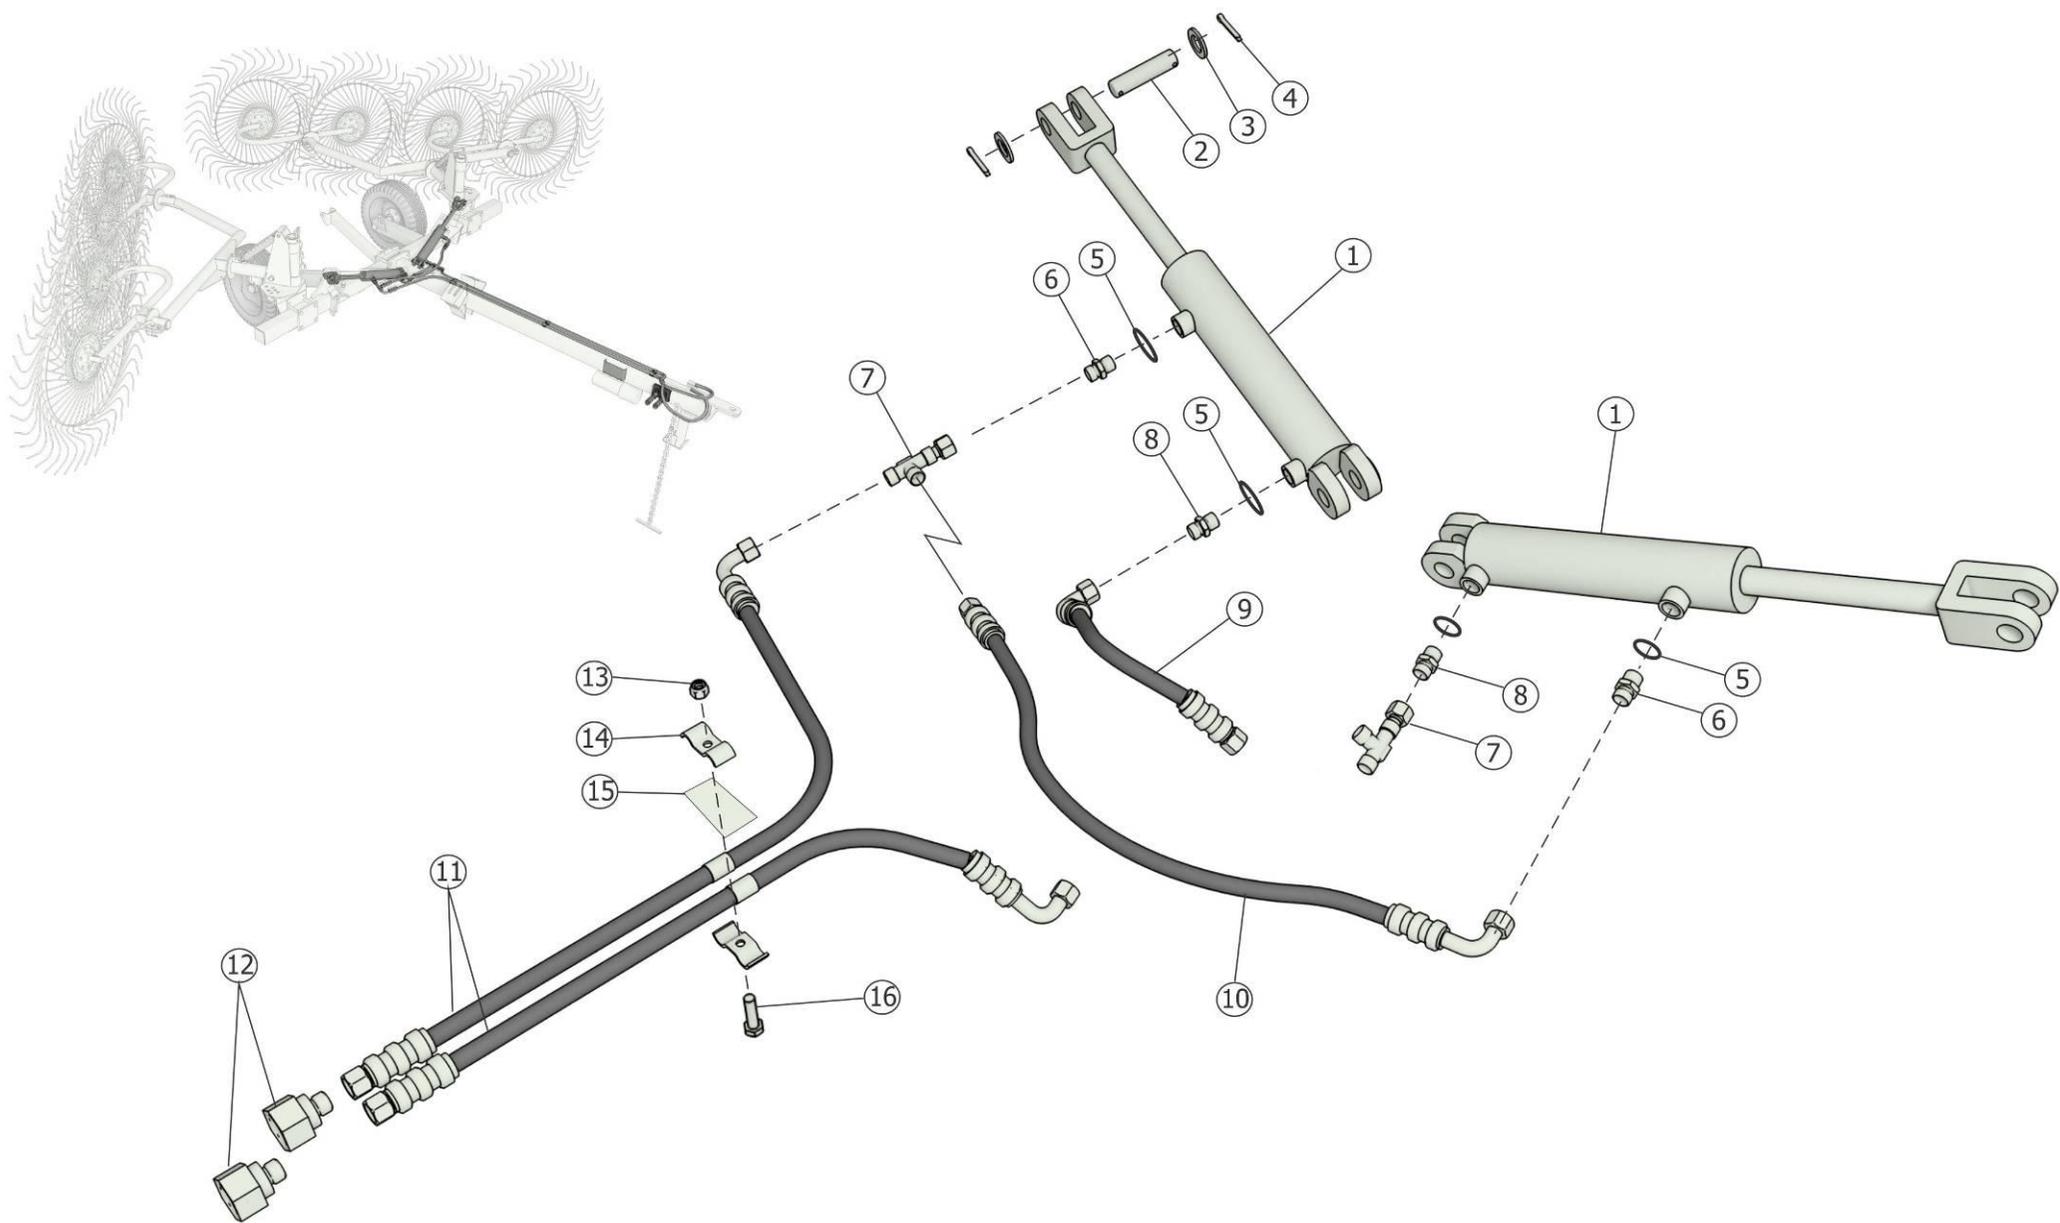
Установка гидравлики ГКП-601.12.000
